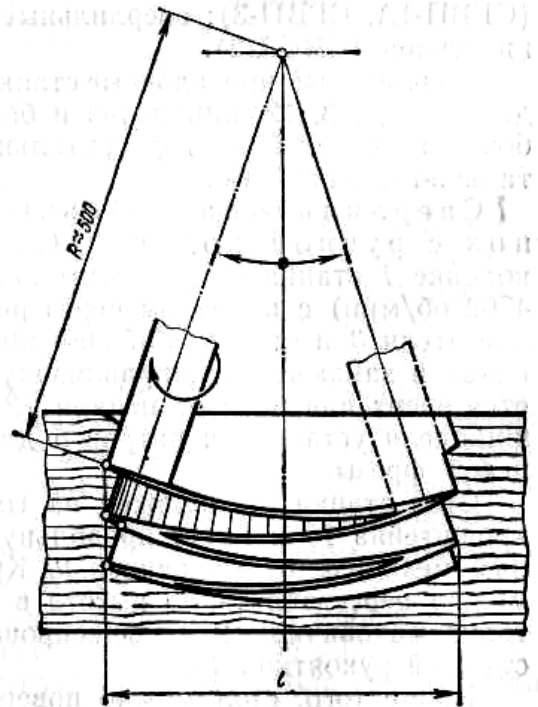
Формирование гнезд на станках с качательным боковым движением фрезы
